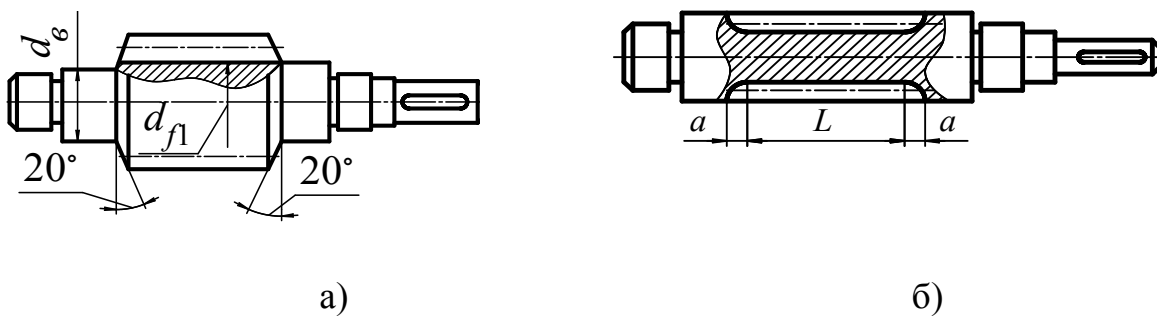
Конструктивные варианты исполнения червяков
